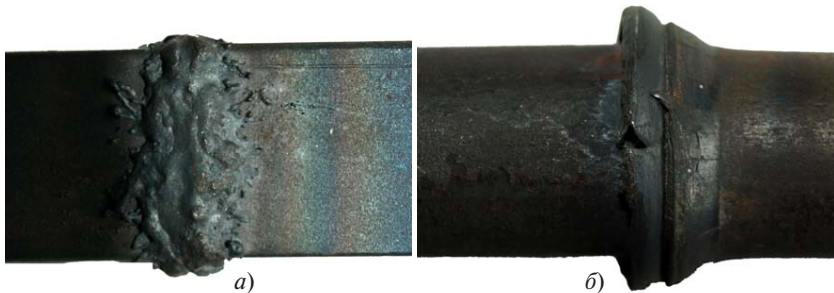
Сварной шов после стыковой сварки (*а*) и сварки трением (*б*)
